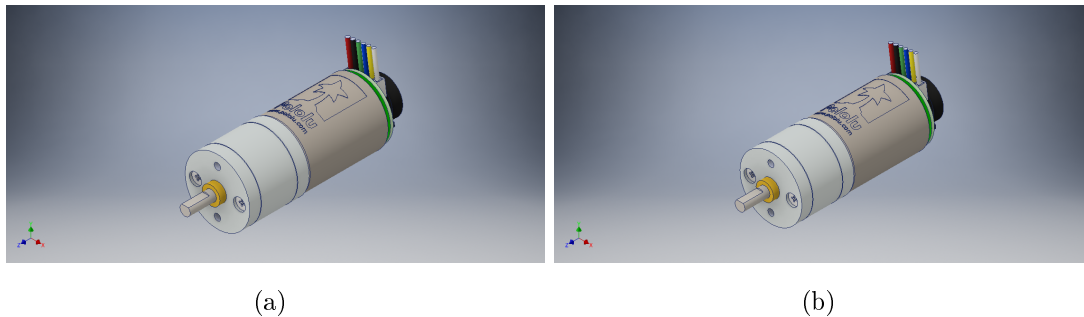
Motores. (a) Motor 1. (b) Motor 2
